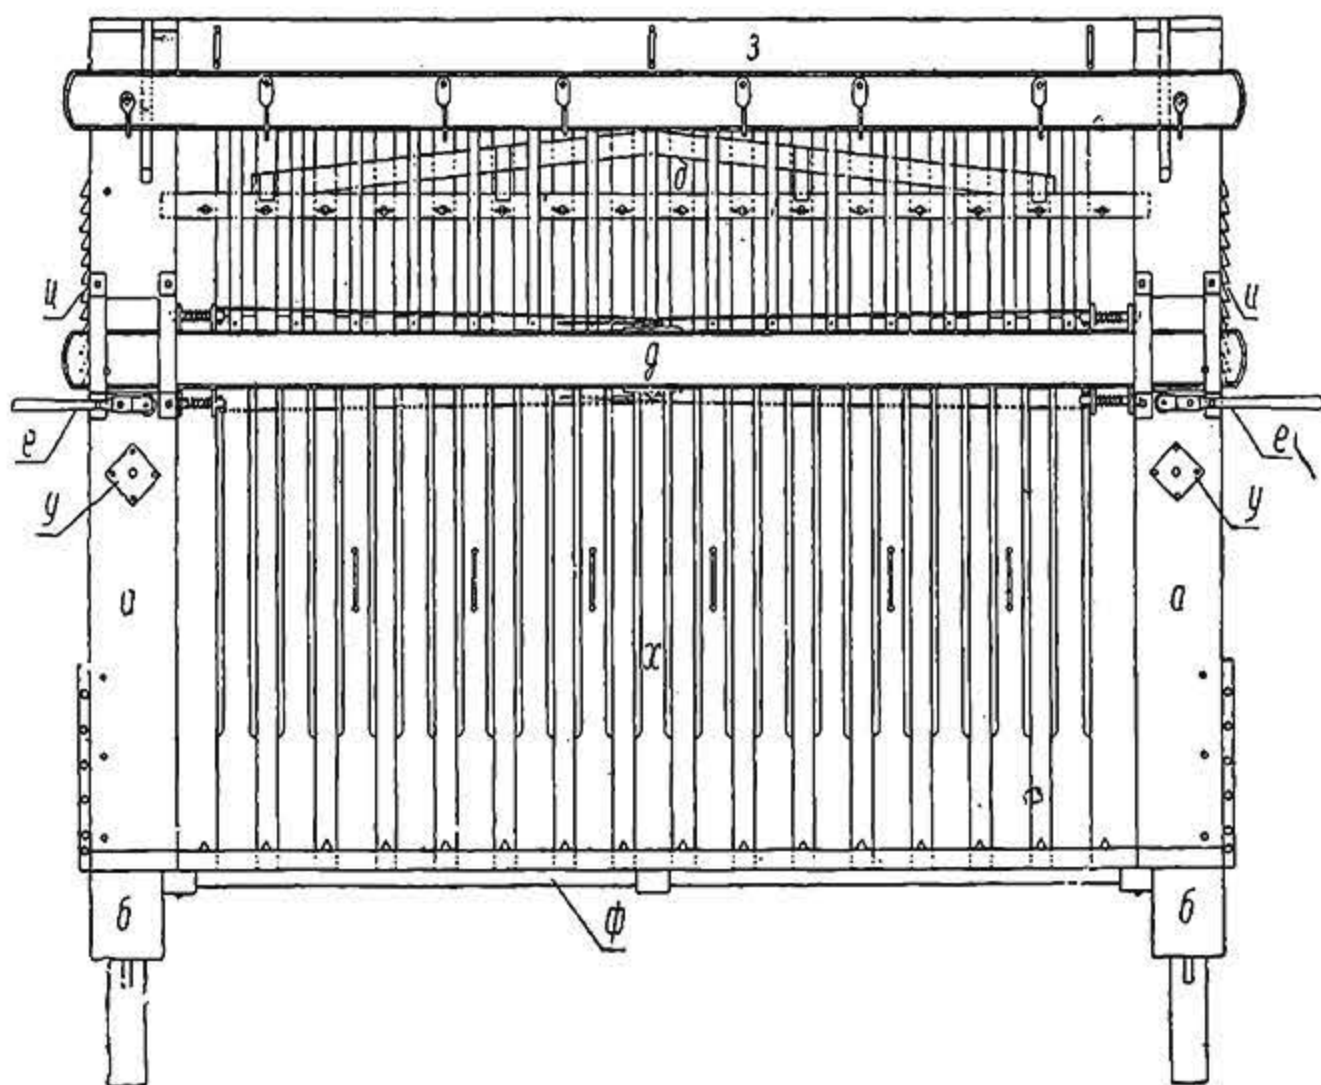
Пресс Черкинского и Фельдмана для приготовления камышитовых (соломитовых) плит — общий вид.
